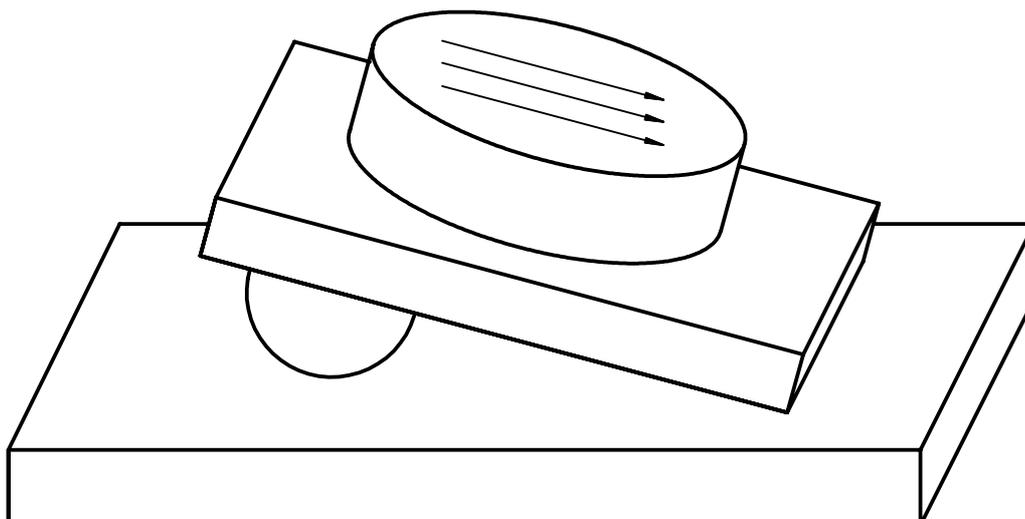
Exemple de verre plan incliné et de plan de mesure
